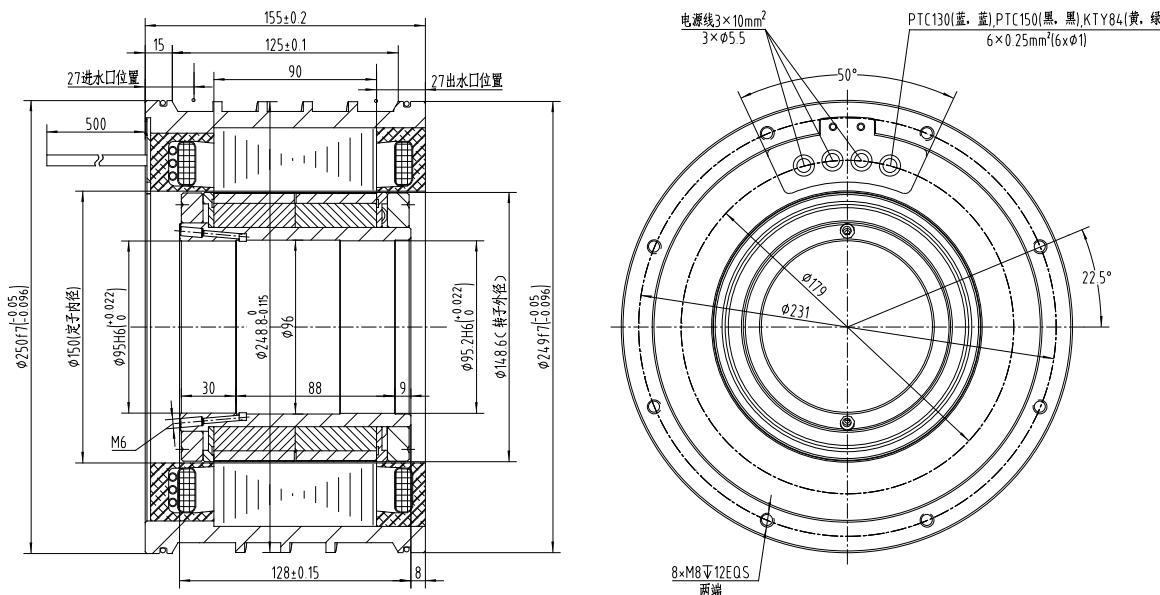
DZT220 系列电动机外形尺寸 (一)
